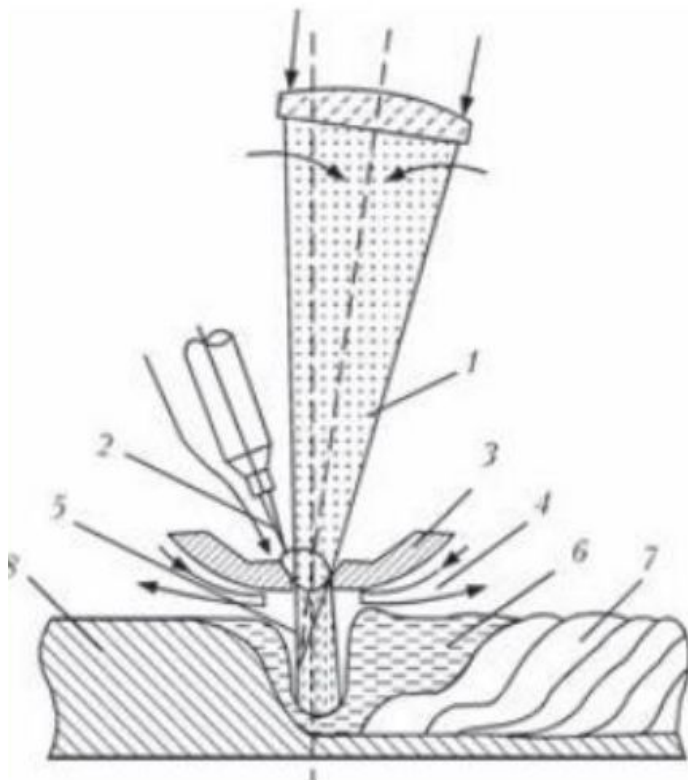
Схема процесса гибридной лазерно-плазменной сварки с расположением плазменной горелки перед лазерным пучком :
